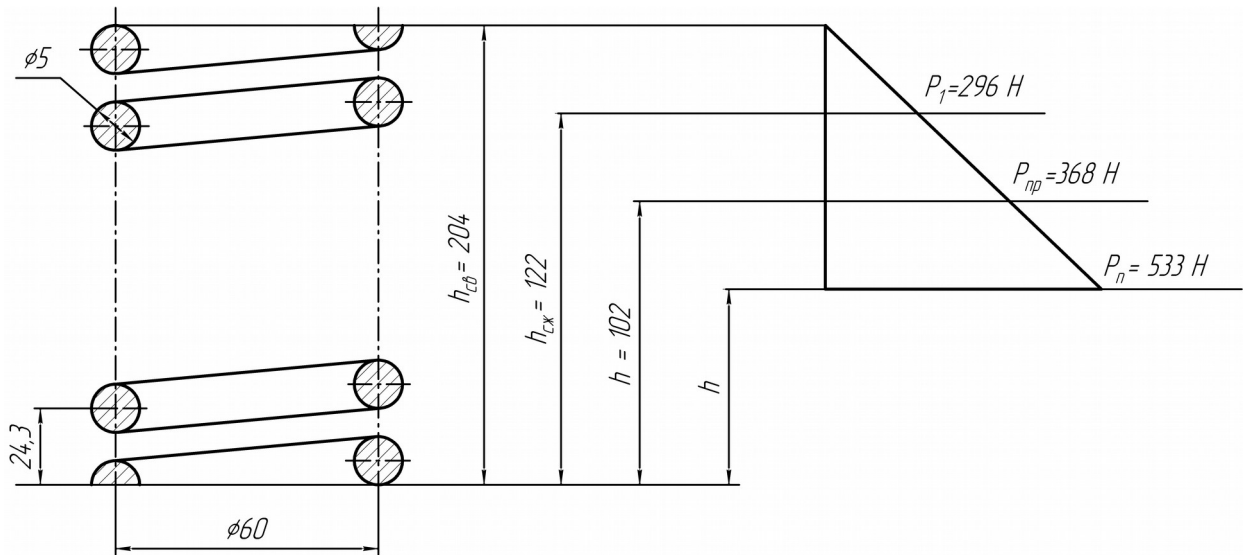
Зворотна пружина поршня гальмового циліндра
